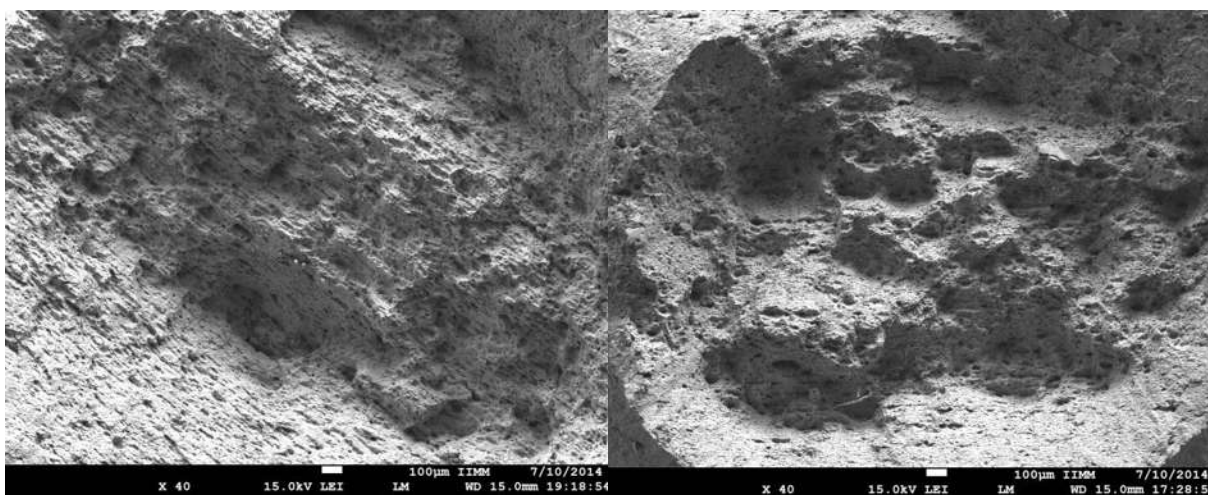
25.- Fractografía de la soldadura 7-1 (cordón de auto-revenido, condición 2).
